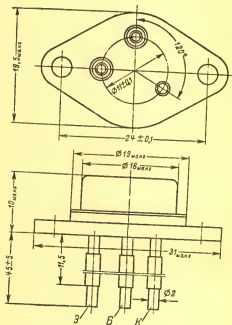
Габаритный чертеж транзисторов П201—П203.
